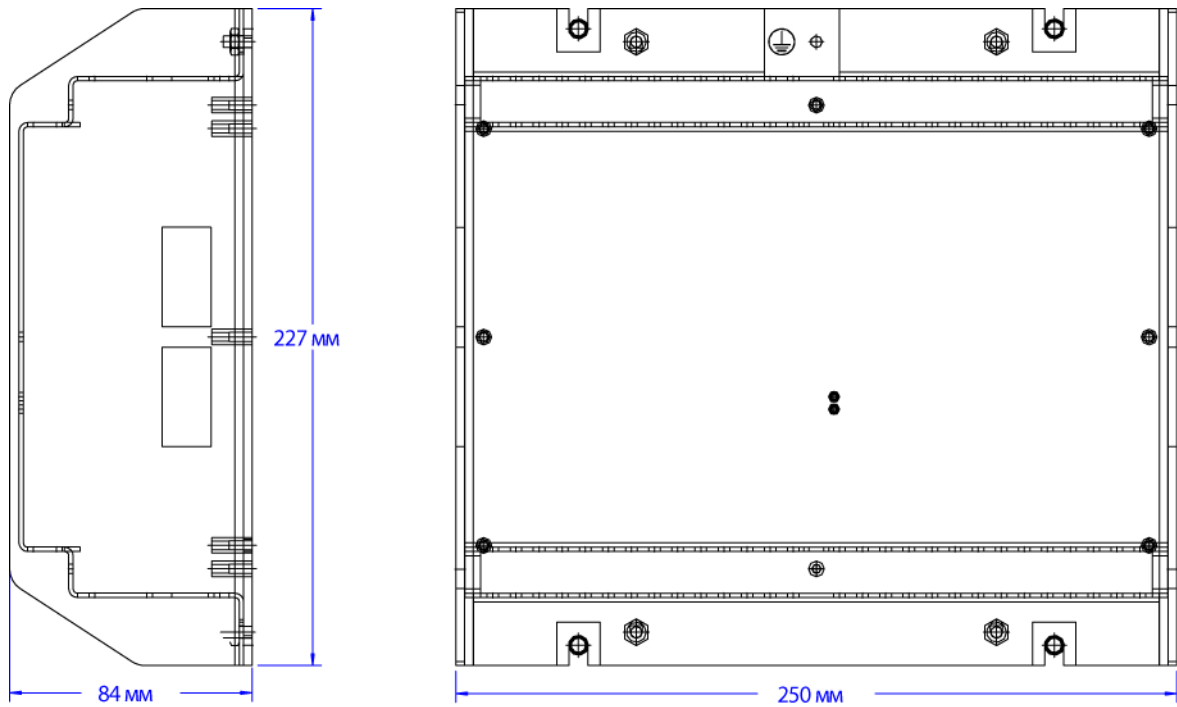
Корпус из листового металла easYgen-3000 - размеры
